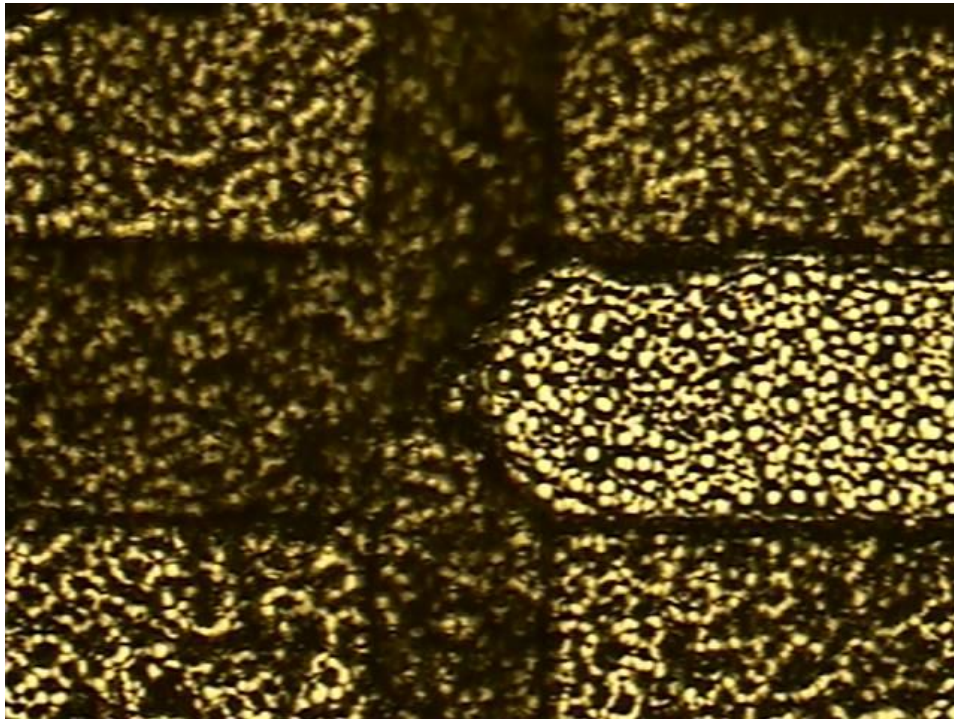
Detalle de las costillas bajas con 160 pasadas
